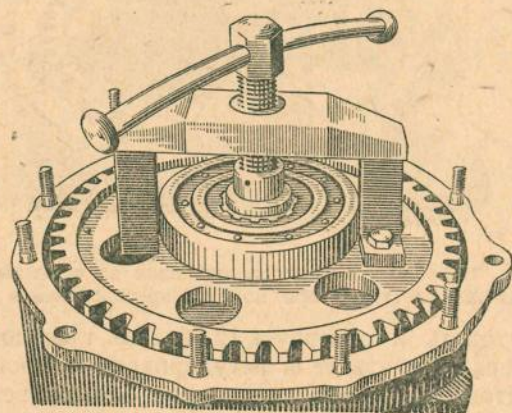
Снятие ведомой шестерни при помощи приспособления
